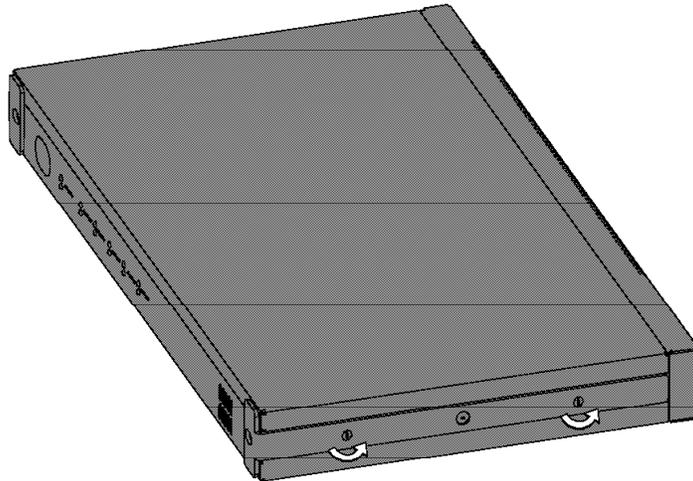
Remoção de Parafusos do Suporte de Montagem
